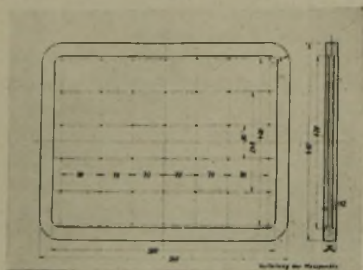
Form und Abmessung der in einem schweren Rahmen fest eingespannten Versuchsplatten aus Ge 12.91, Ge 22.91 und Ge 32.91
